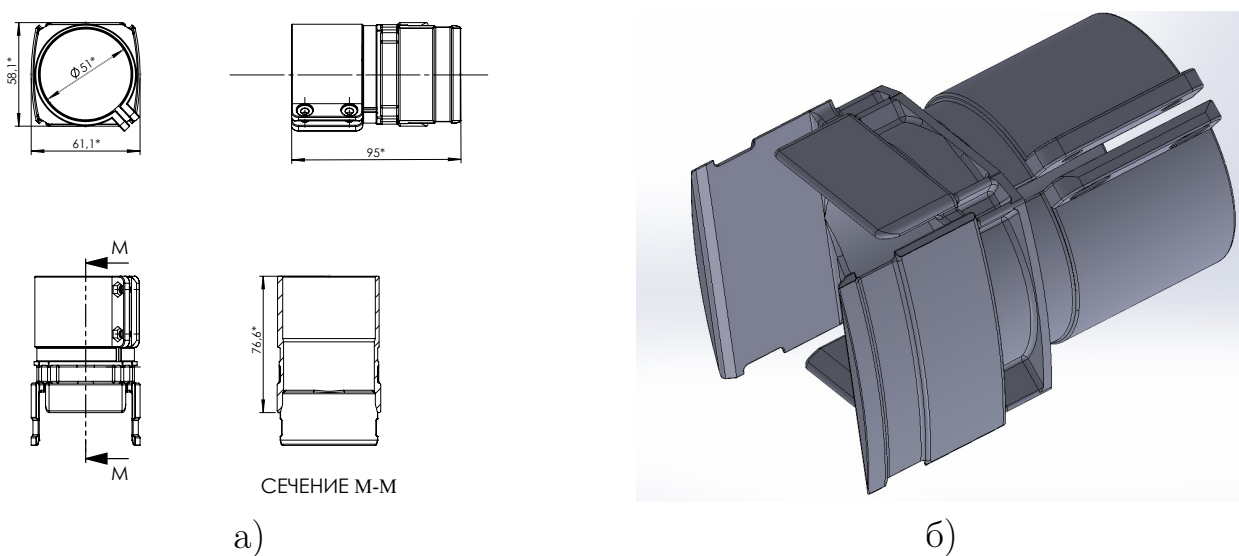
а) Чертеж детали, обеспечивающей крепеж ФЭУ с сцинтиллятором. б) 3D-модель детали.
